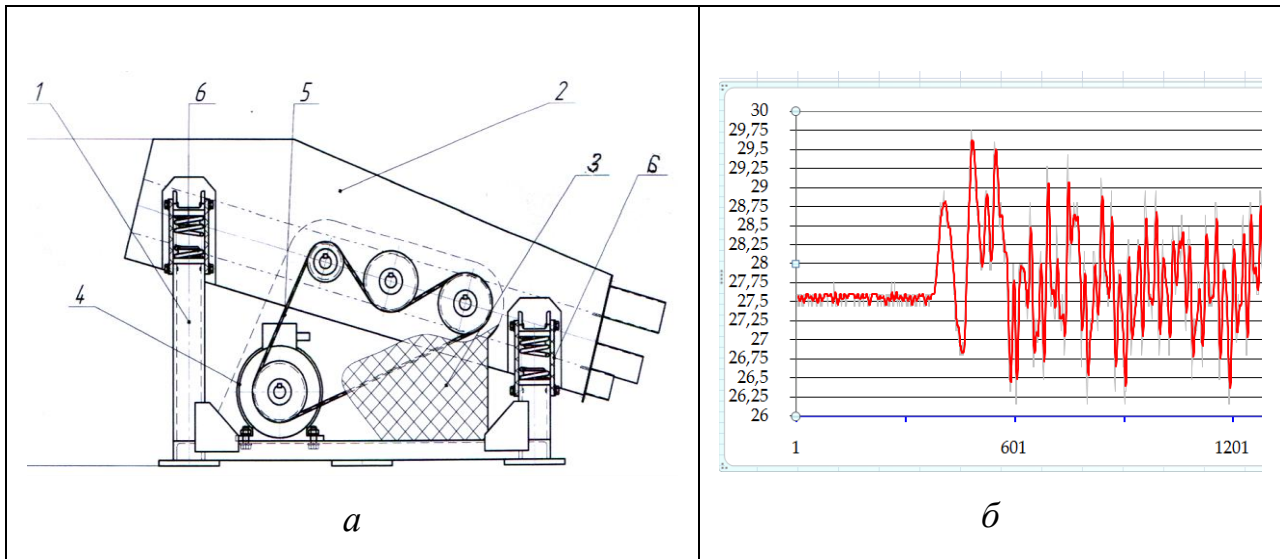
Конструктивна схема інерційного грохоту (а) та фрагмент віброграми вертикальних коливань корпусу (б): 1 – станина; 2 – короб; 3 – кожух; 4 – двигун; 5 – зубчасто-пасовий привод; 6 – амортизатори
